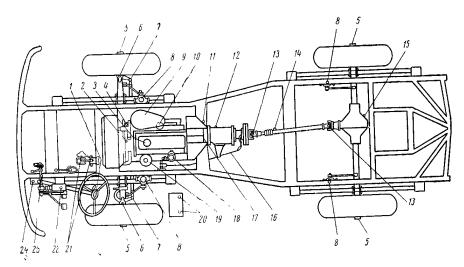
Схема смазки авгомобилей УАЗ-451М
